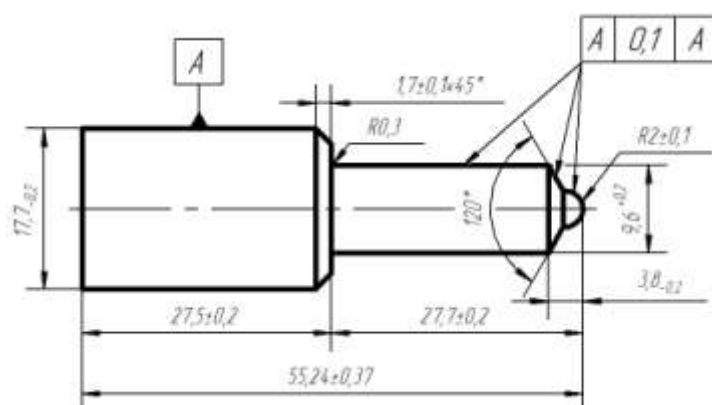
Эскиз поковки «корпус распылителя»
